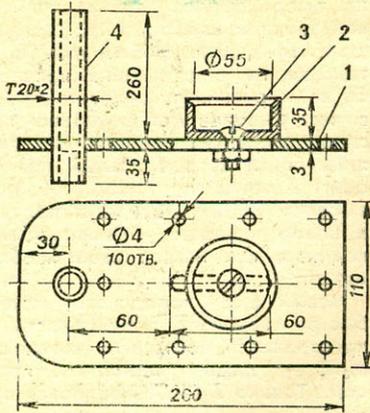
Планка: 1 — основание, 2 — подвижный степс мачты, 3 — винт с гайкой, 4 — труба (подшипник рулевого вала).
